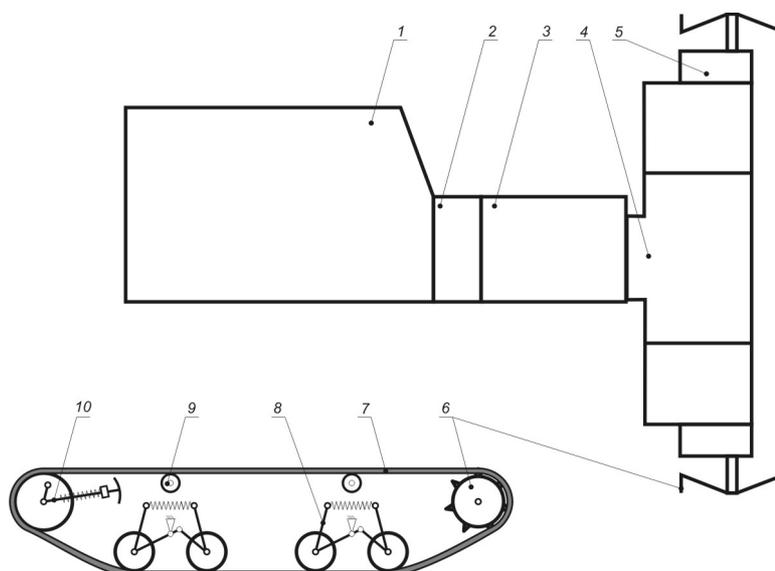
Кинематическая схема гусеничной машины: 1 – двигатель внутреннего сгорания (ДВС); 2 – сцепление; 3 – коробка перемены передач; 4 – задний мост с главной передачей и дифференциальным механизмом; 5 – бортовой редуктор; 6 – ведущая звездочка; 7 – гусеничная цепь; 8 – каретка; 9 – поддерживающий ролик; 10 – натяжной механизм
